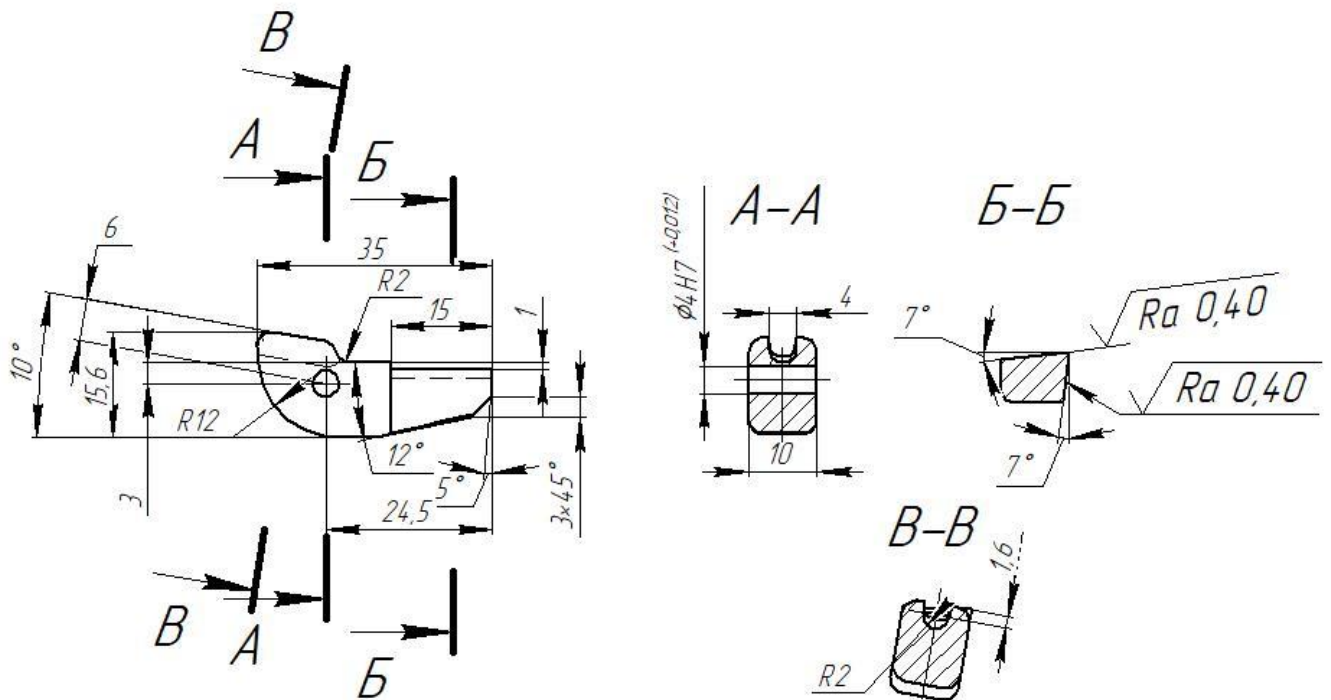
Ескіз змінної пластини зворотньої цековки
